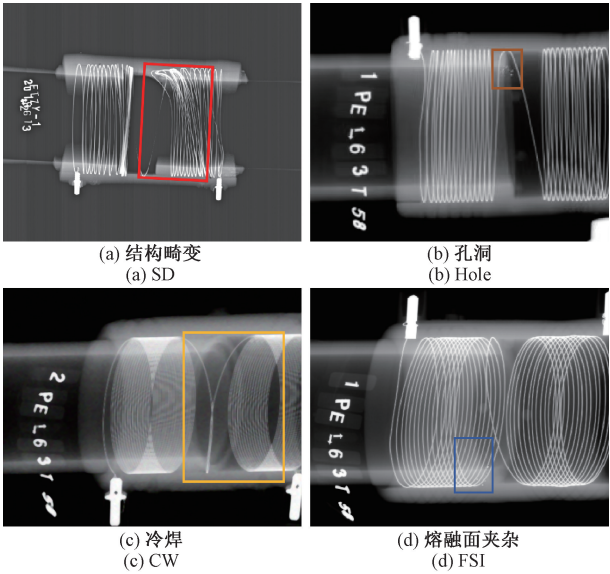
部分采集的电熔焊接缺陷 DR 图像
